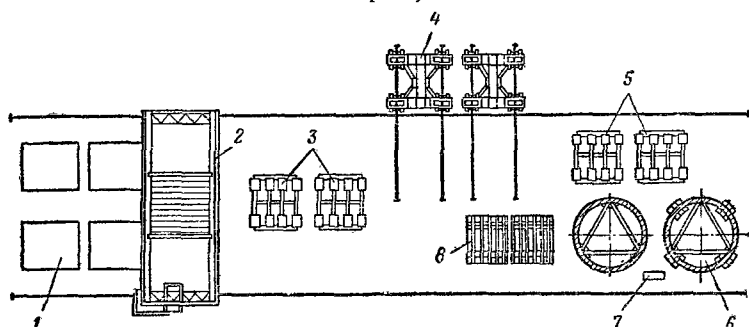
Площадка для укрупнительной сборки и сварки обечаек цементных печей
